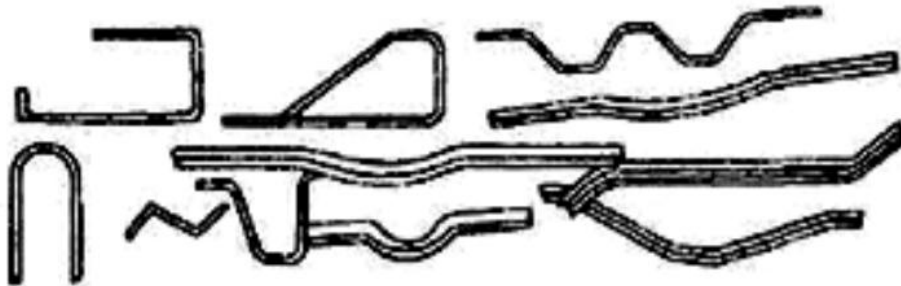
Типові деталі, що виготовлені на згинальних машинах
